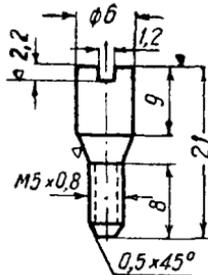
Дет. № 312. Упорный винт кулачка дроссельной заслонки
